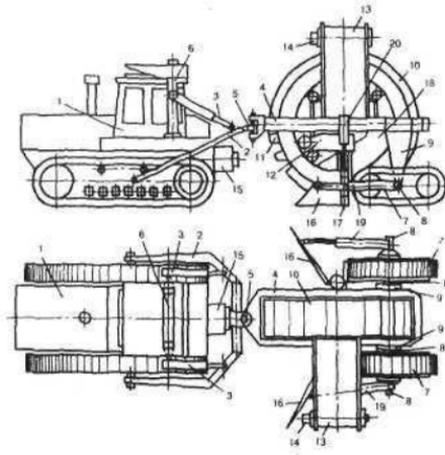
Конструктивная схема выемочно-погрузочного агрегата: 1- базовая машина; 2- рама базовой машины; 3- гидроцилиндры; 4- рама рабочего органа; 5- двойной шарнир; 6- защитный каркас; 7- шасси; 8- ось шасси; 9- кронштейны; 10- ротор; 11- ковш ротора; 12- привод; 13- ленточный конвейер; 14- привод ленточного конвейера; 15- гидравлический насос; 16- лемехи; 17- шарнир; 18- плита рамы рабочего органа; 19, 20- гидроцилиндры
